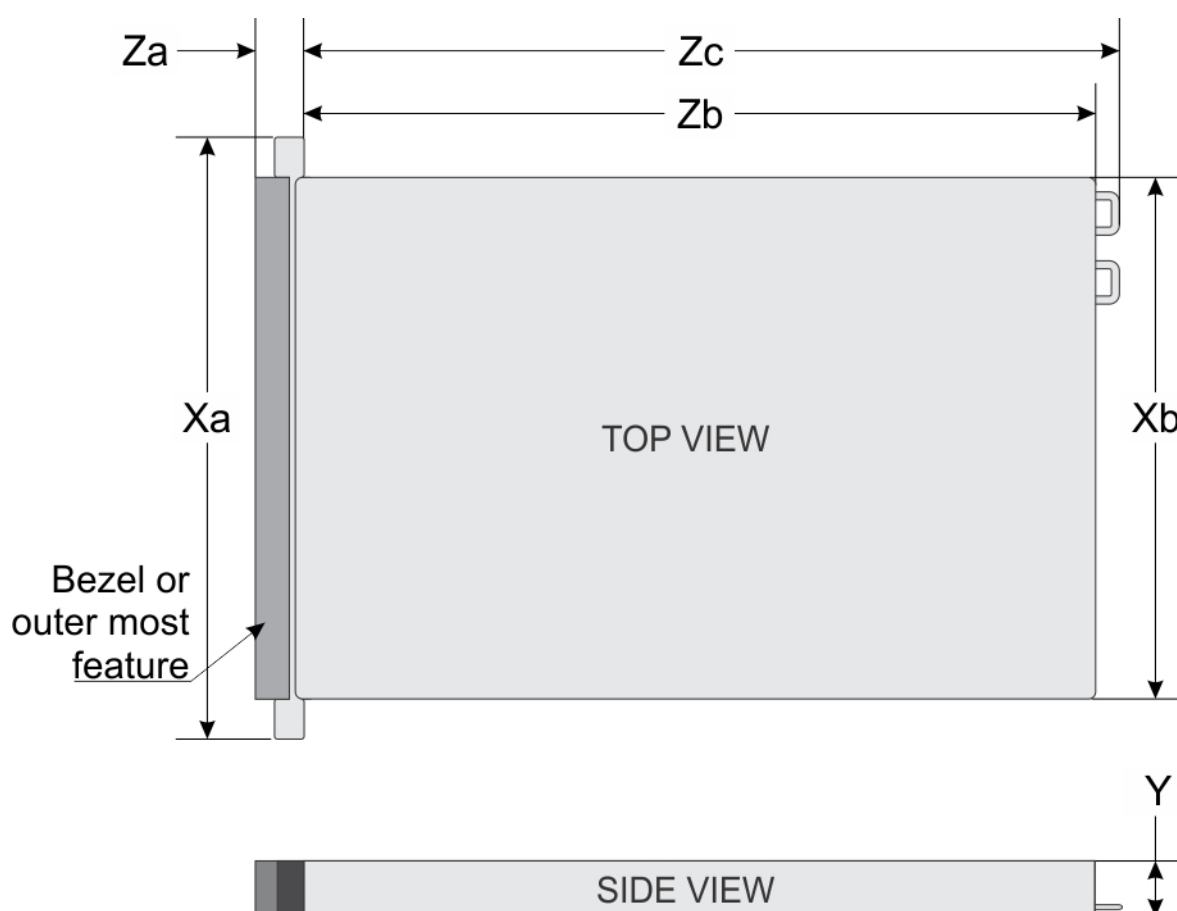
Dimensioni dello chassis di PowerEdge R750xs
